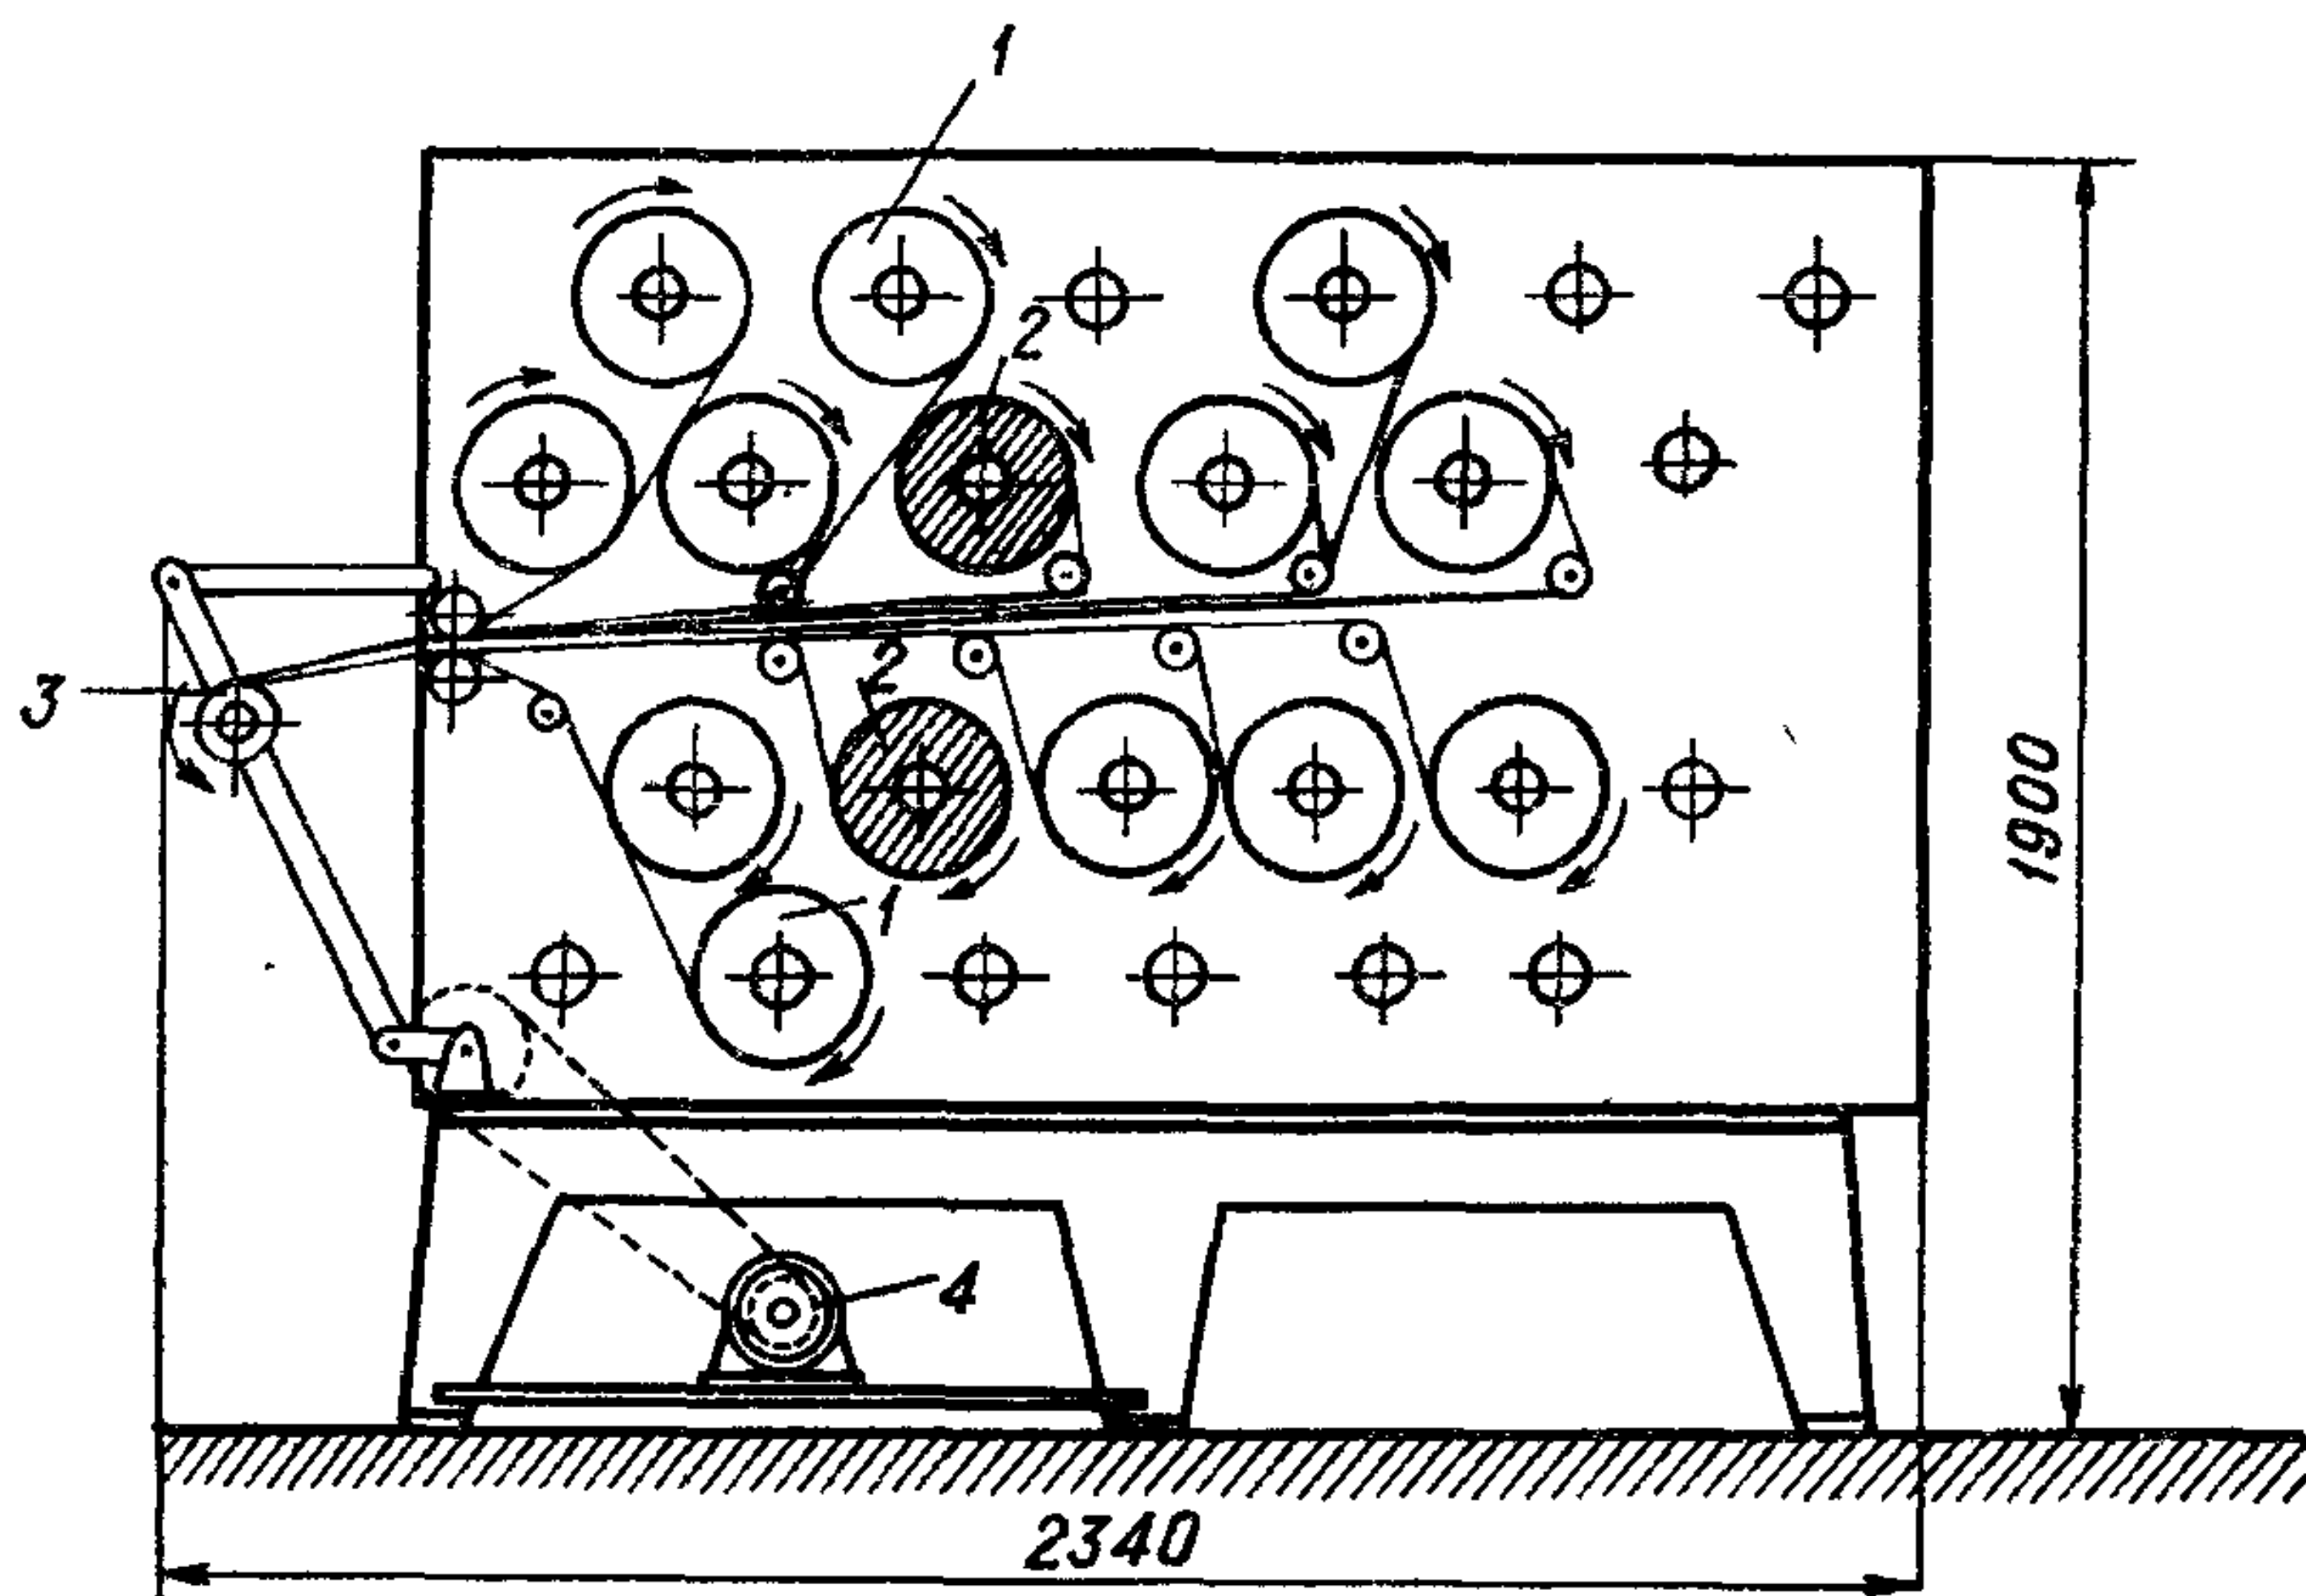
Схема устройства 24-шпиндельного намоточного станка для намотки секций силовых конденсаторов.
